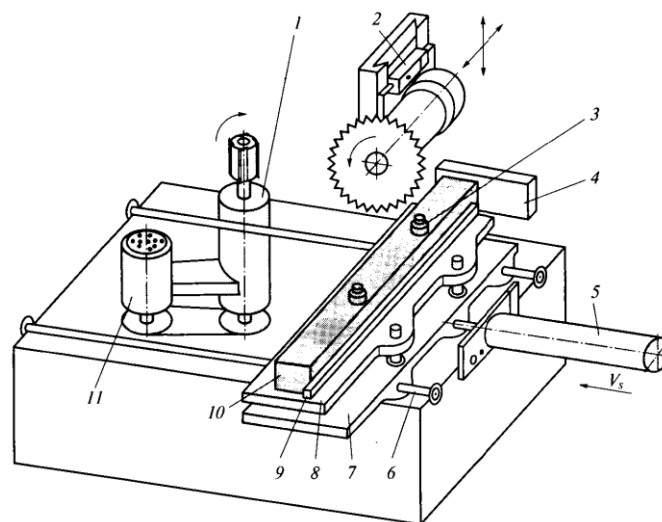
Шипорізний верстат для виробітку клинових шипів: 1 – фрезерний супорт; 2 – пильний супорт; 3 – гідропритиск; 4 – торцевий упор; 5 – гідроциліндр; 6 – напрямна; 7 – основна каретка; 8 – стіл; 9 – базувальна лінійка; 10 - заготовка; 11 - електродвигун
